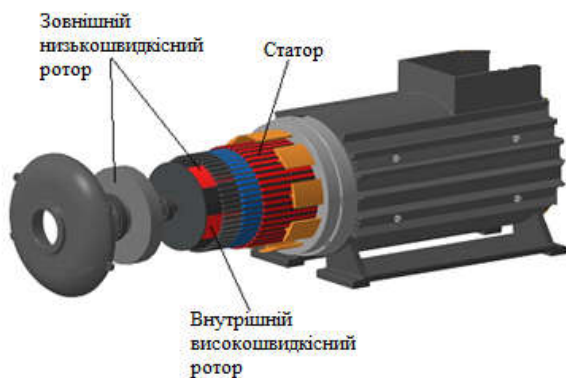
Базова конструкція гібридного магнітного редуктора-генератора
